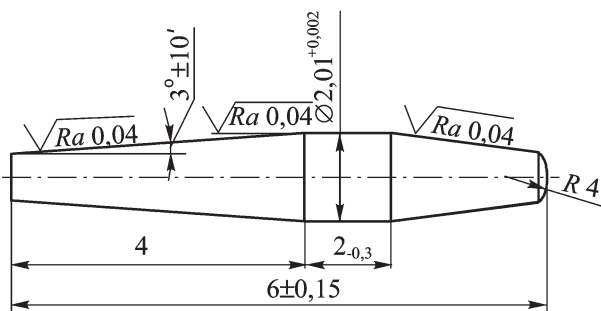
Твердосплавный однозубый дорн малого диаметра
